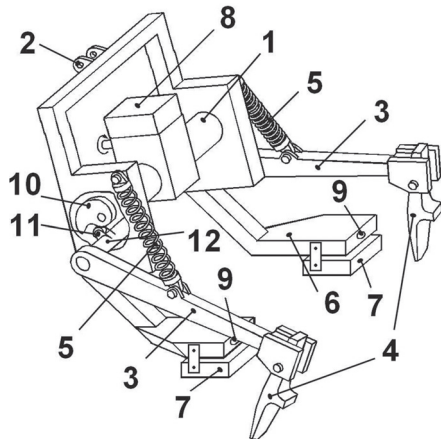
Лункообразователь типа Л-2М с установленным пневматическим высевающим приспособлением
